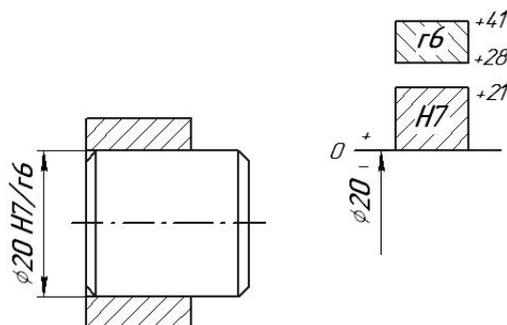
Посадка с натягом и схемы расположения полей допусков
